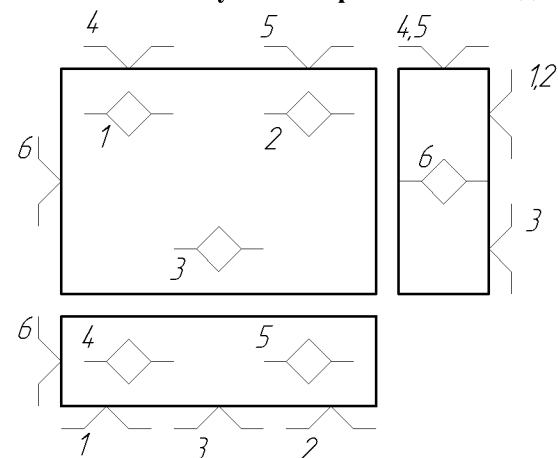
Теоретична схема базування призматичних деталей: 1,2,3 – установча база; 4,5 – напрямна база; 6 – опорна база
